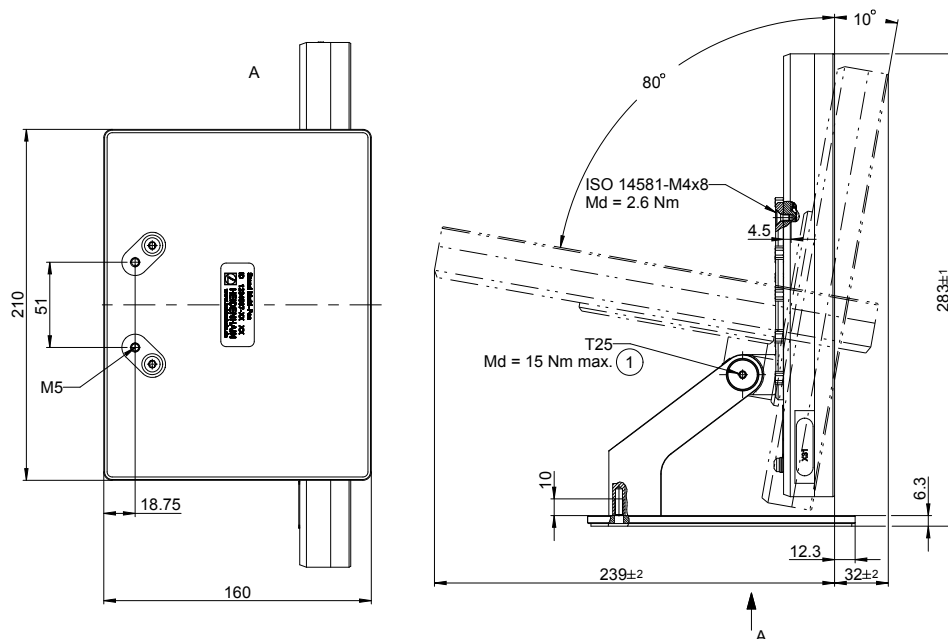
Dimensões do aparelho com pé de suporte Multi-Pos
